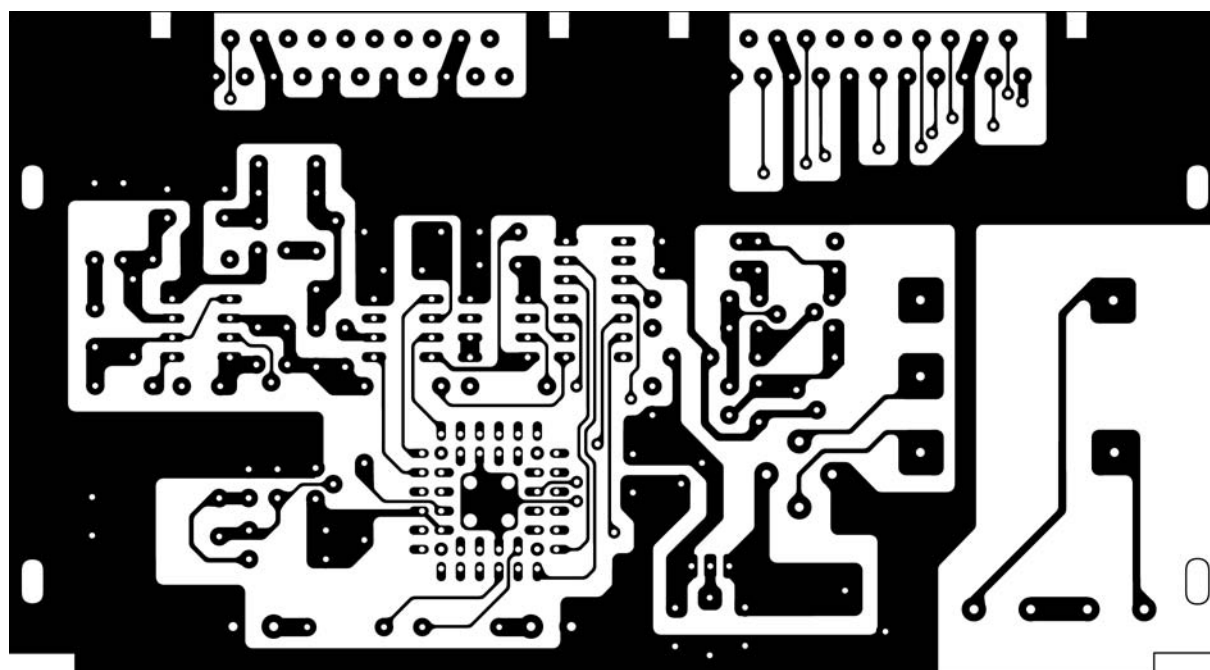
2: Dessin, à l'échelle 1, de la face "soudures".
